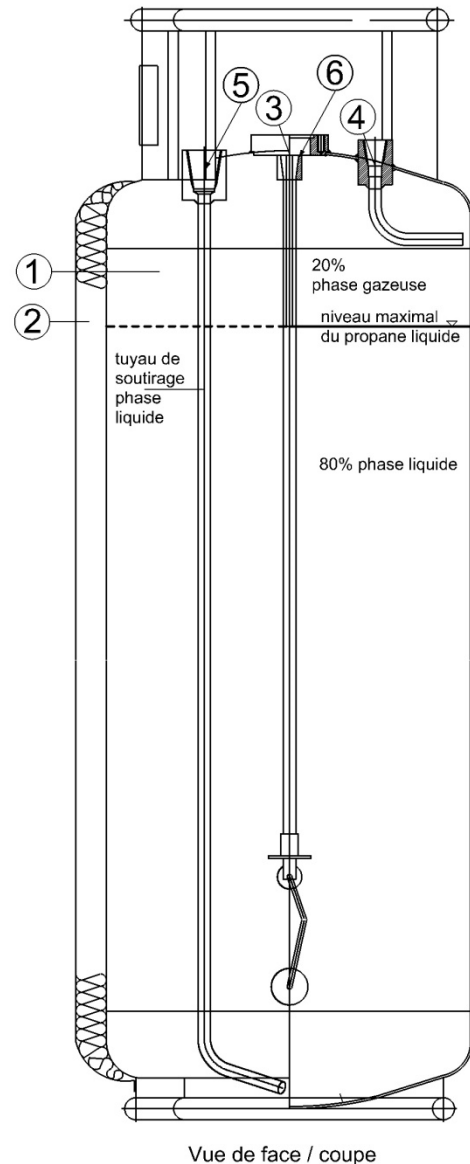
Vue de coupe d'un cylindre à gaz
